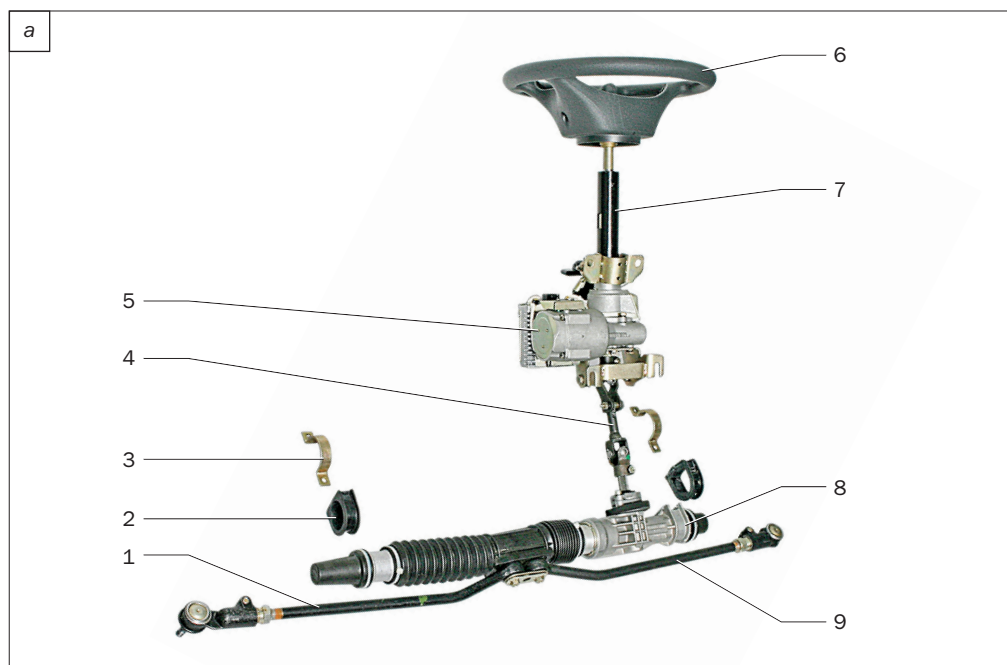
а. Реечный рулевой механизм: 1 — правая рулевая тяга в сборе; 2 — опора рулевого механизма; 3 — скоба опоры рулевого механизма; 4 — промежуточный карданный вал; 5 — электроусилитель; 6 — рулевое колесо; 7 — рулевая колонка; 8 — рулевой механизм; 9 — левая рулевая тяга в сборе
